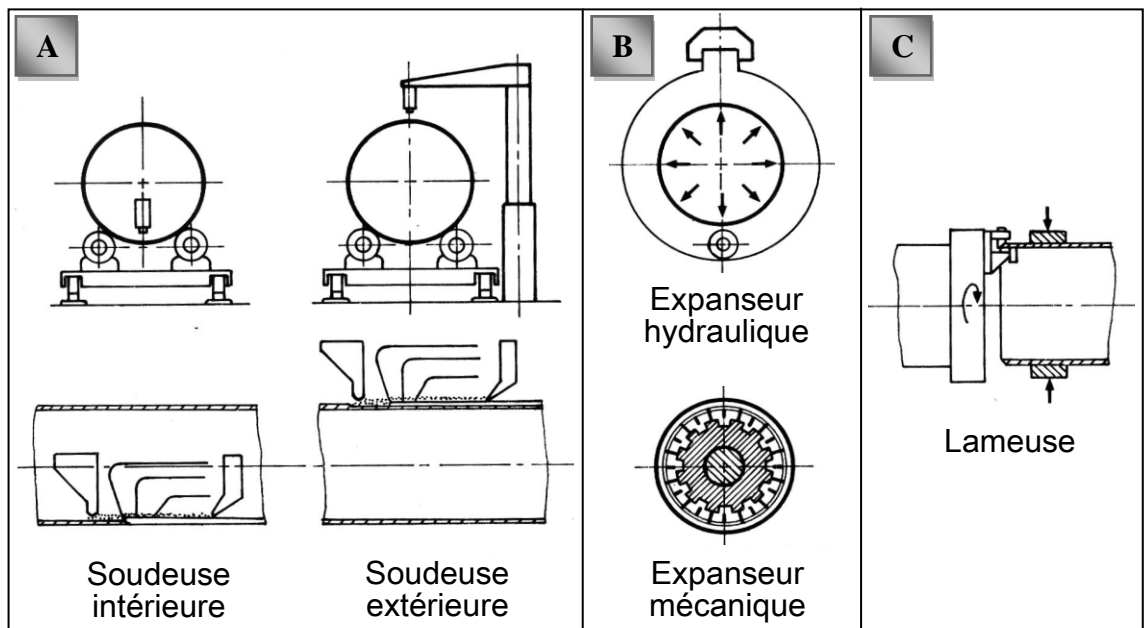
Soudage et finition des tubes par le procédé « UOE », [16]
